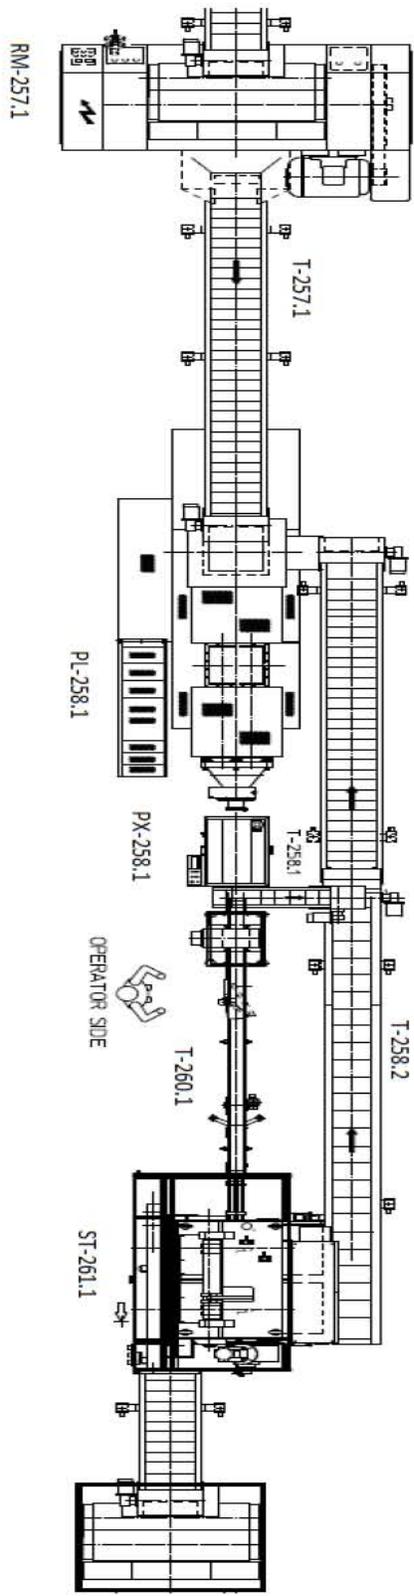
Plano de jabón en fábrica La Corona – Vista en Planta.
